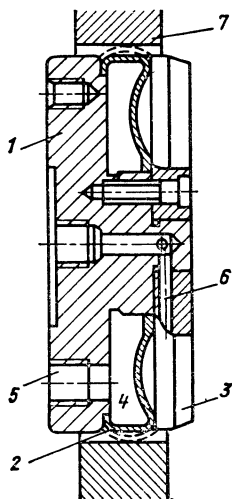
Разжимная оправка для базирования блоков цилиндров по отверстиям под коленчатый вал
